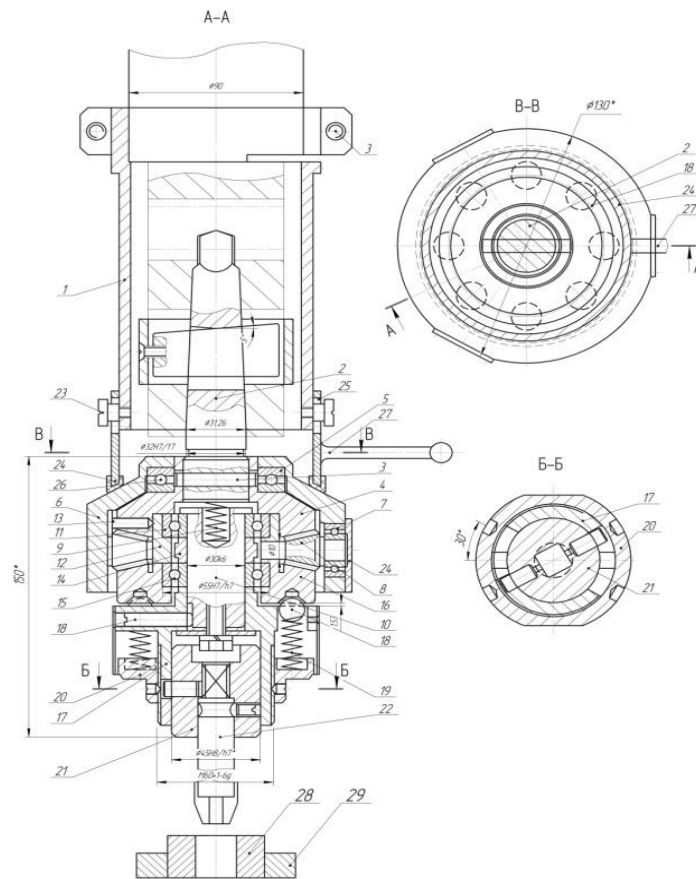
Реверсивний пристрій для нарізання гайок з зігнутим хвостовиком
